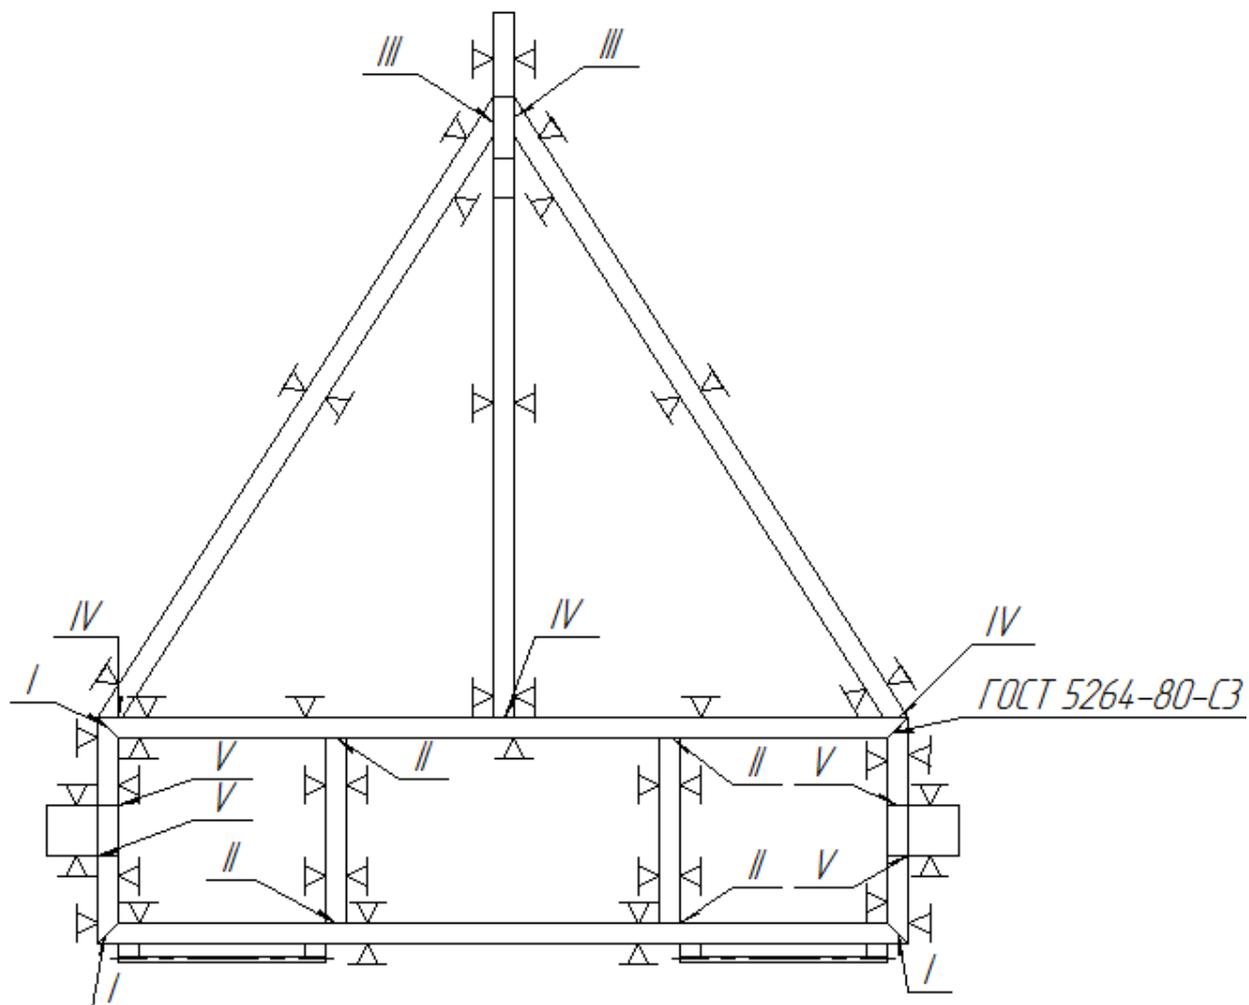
Схема приспособлений для сборки автомобильного подката
